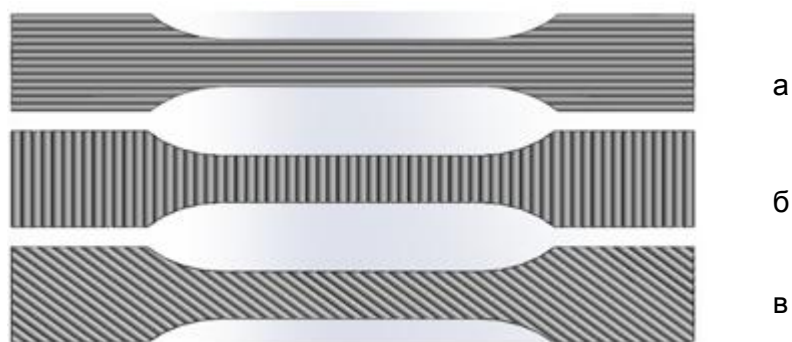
Внешний вид образцов, изготовленных разными способами 3D-печати:
